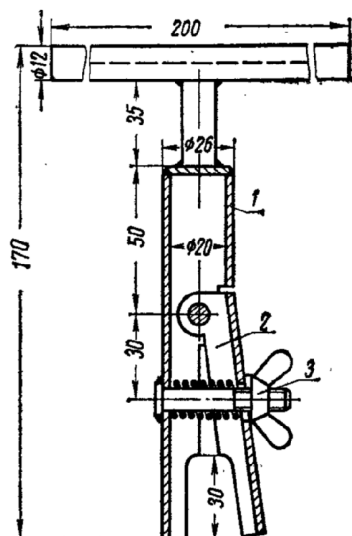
Приспособление с цилиндрической разрезной гайкой:
